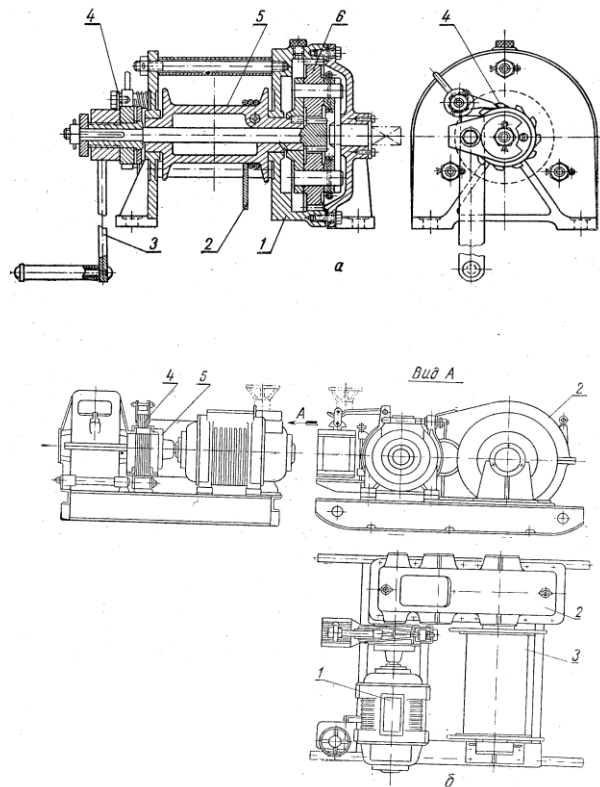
Лебідки: а – з планетарним механізмом; 1 – корпус; 2 – канат; 3 – рукоятка; 4 – стопорно-гальмівний пристрій; 5 – барабан; 6 – передавальний механізм; б – лебідка з електроприводом: 1 – електродвигун; 2 – редуктор; 3 – барабан; 4 – гальмівний пристрій; 5 – муфта.
